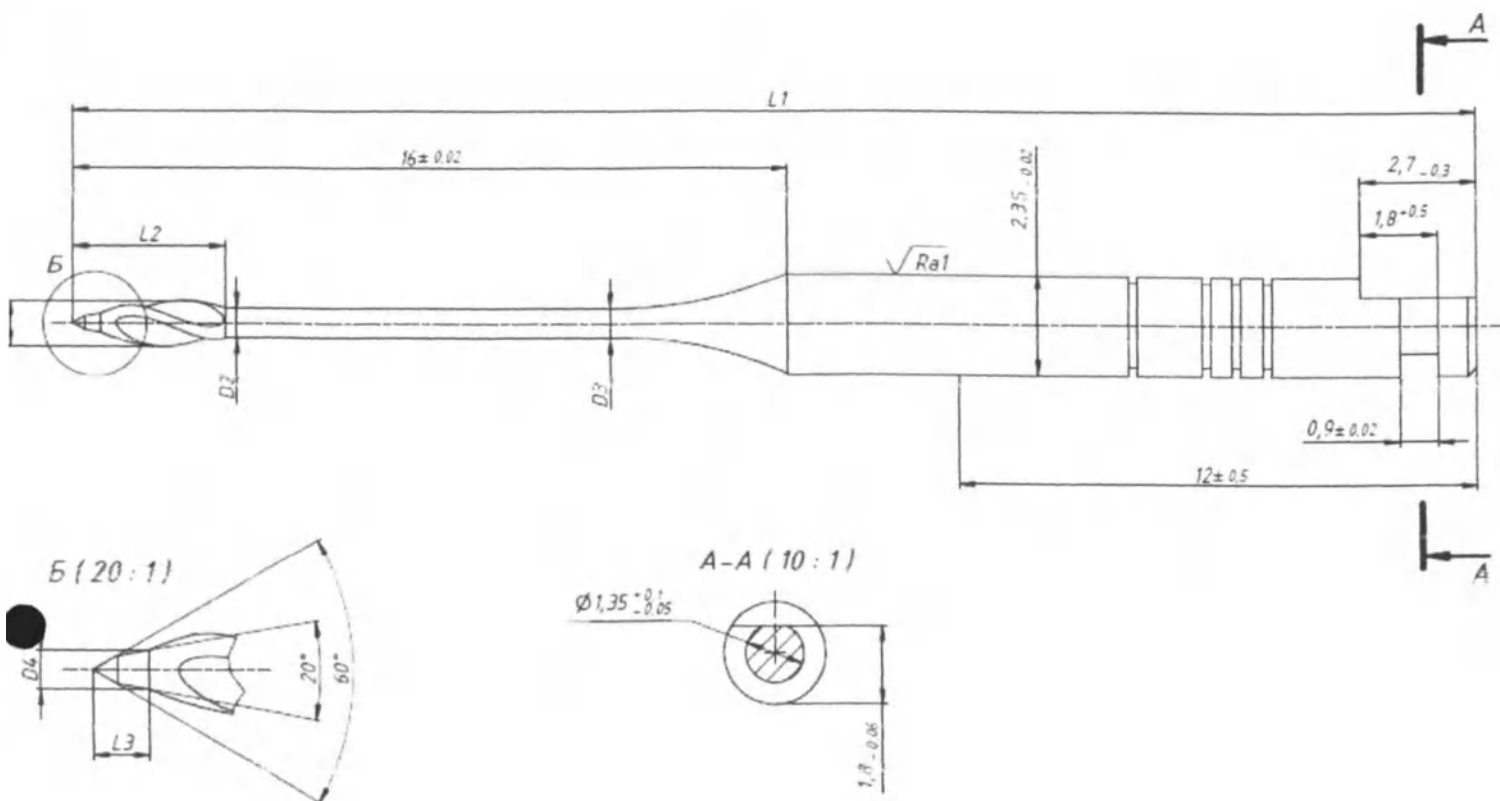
Общий вид бора типа SCF-SS. Gates Drills Rotary.
